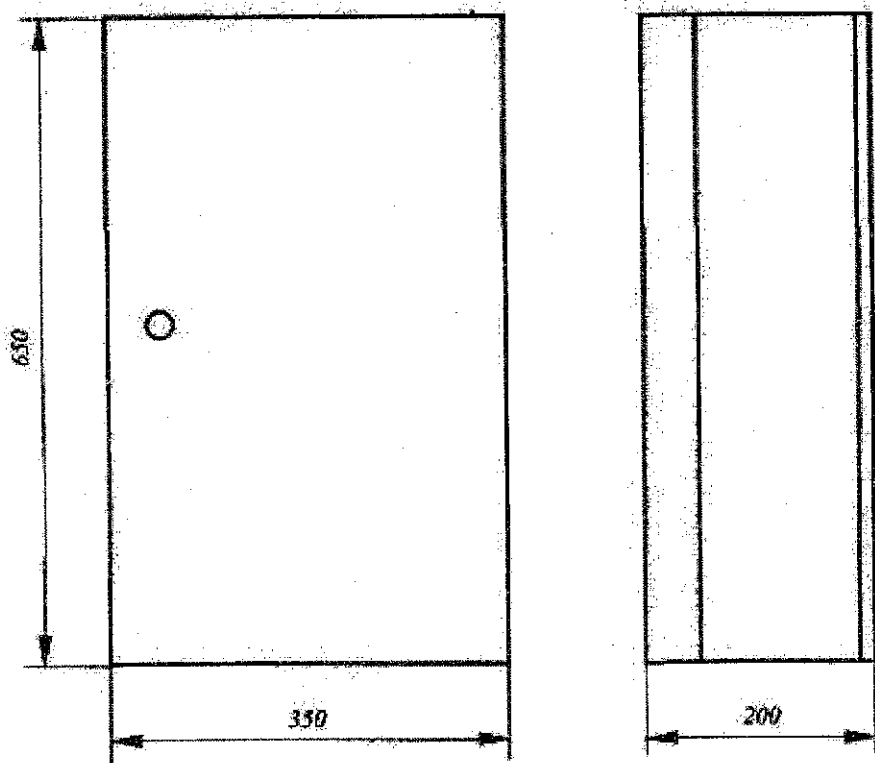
Габаритные размеры щитка коттеджного ЯВУ-01К-40-УЗ
